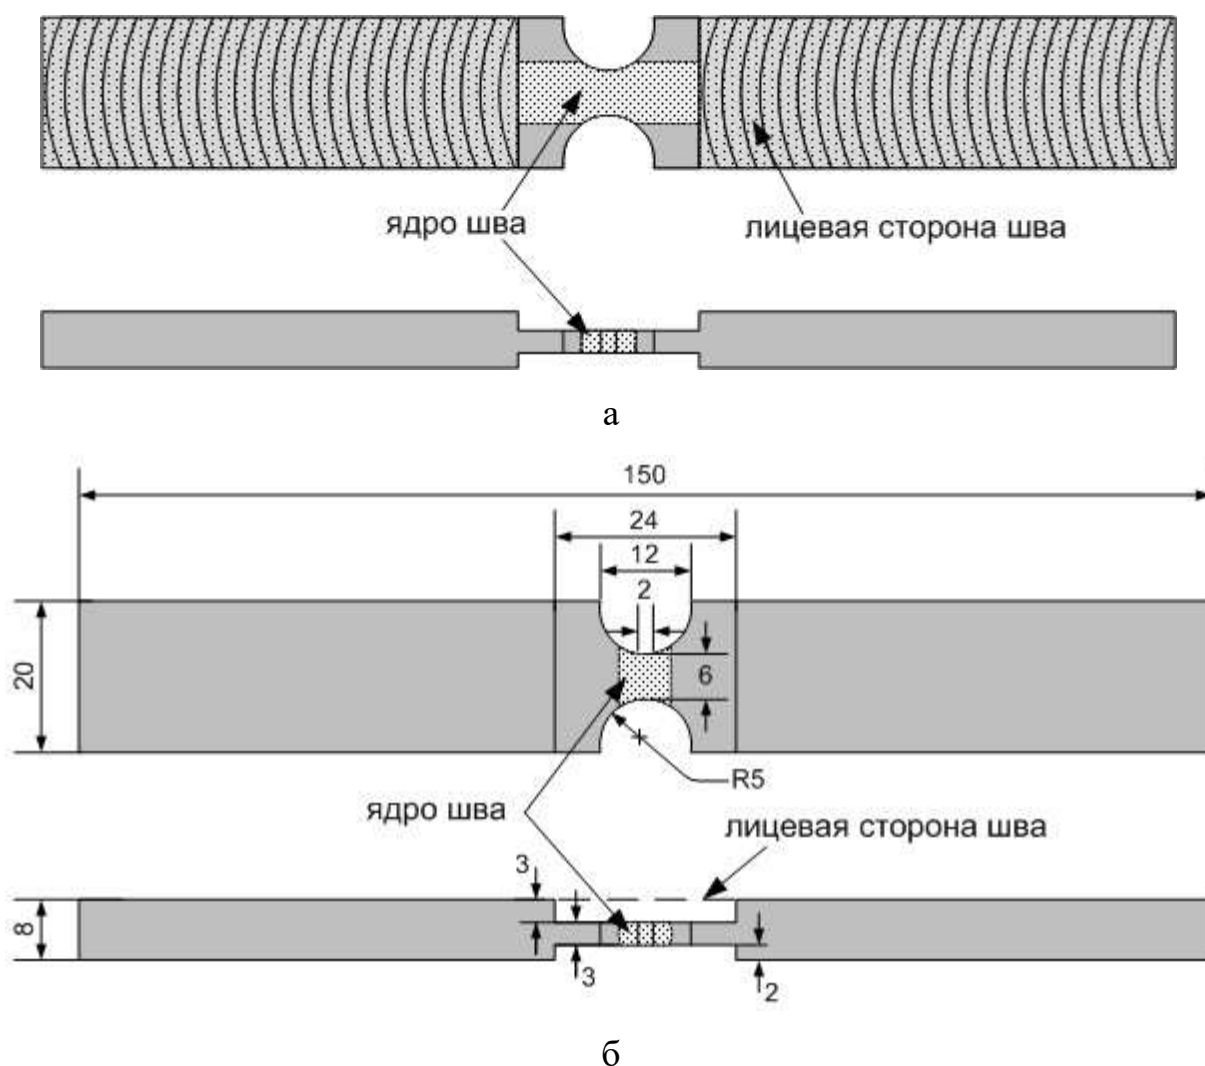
Схема вырезки образцов из ядра сварного шва:
